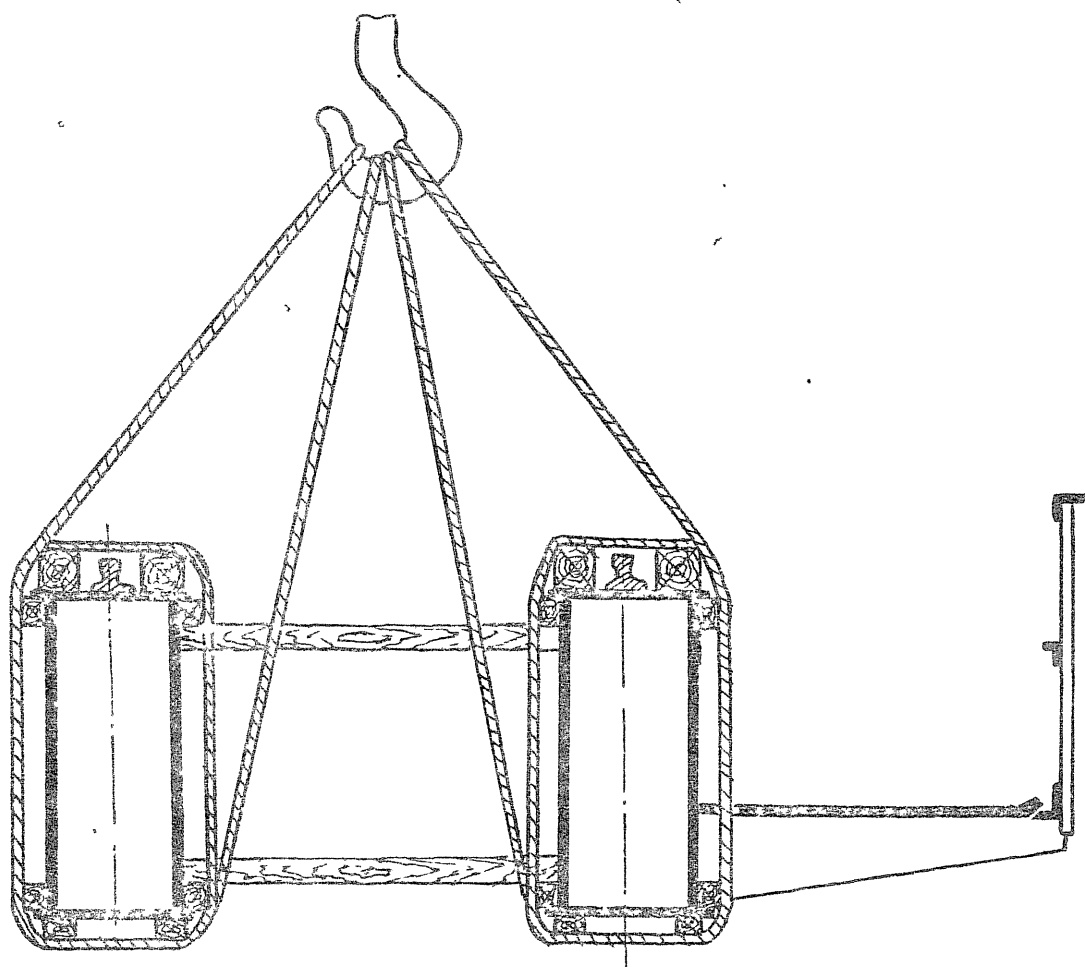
Стропильная моста при подъеме на месте монтажа крана.
